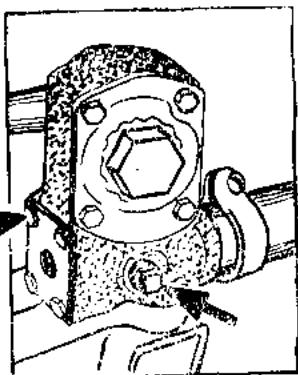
Рулевой механизм. Стрелка указывает место слива масла.
